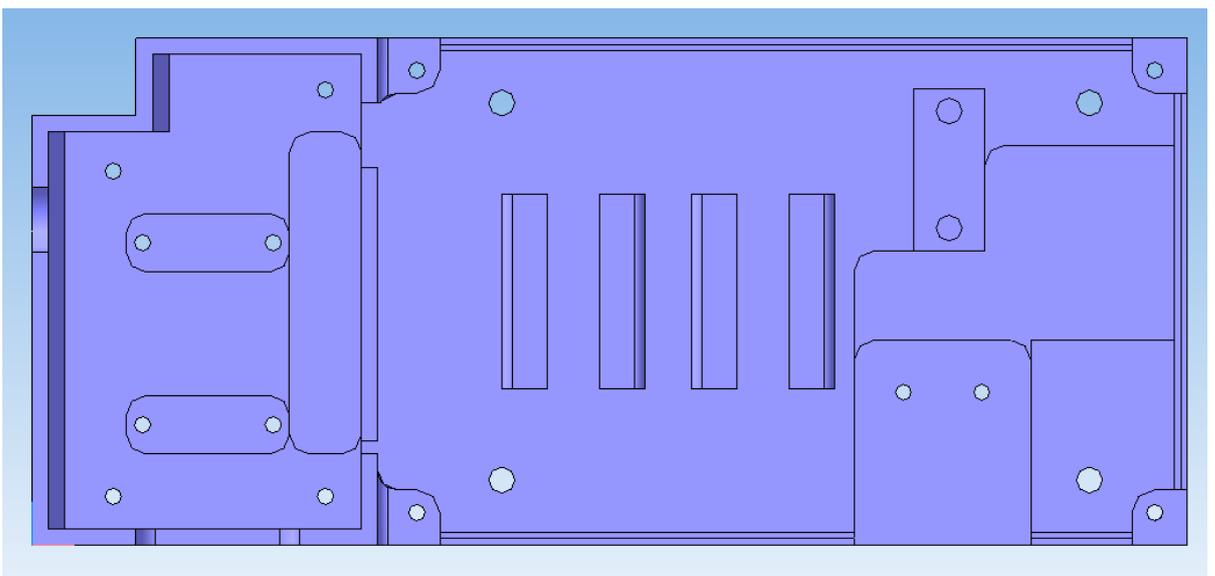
Трехмерная модель корпуса координатно-измерительной машины Mora Primus (вид снизу)
